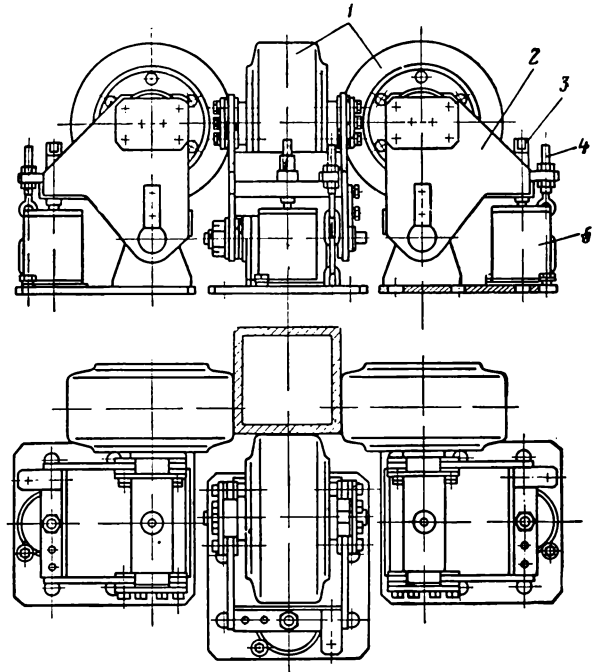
Общий вид блока роликоопоры типа НКК конструкции института Донгипроуглемаш:
